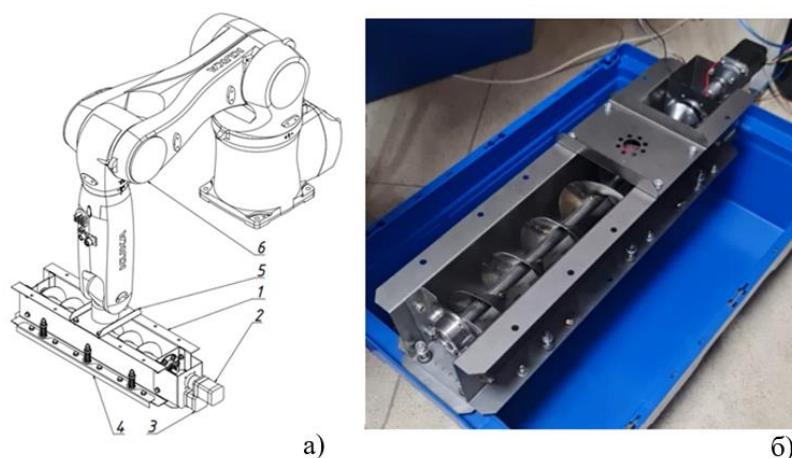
Схема установки с шиберной заслонкой а) и фото установки б)
